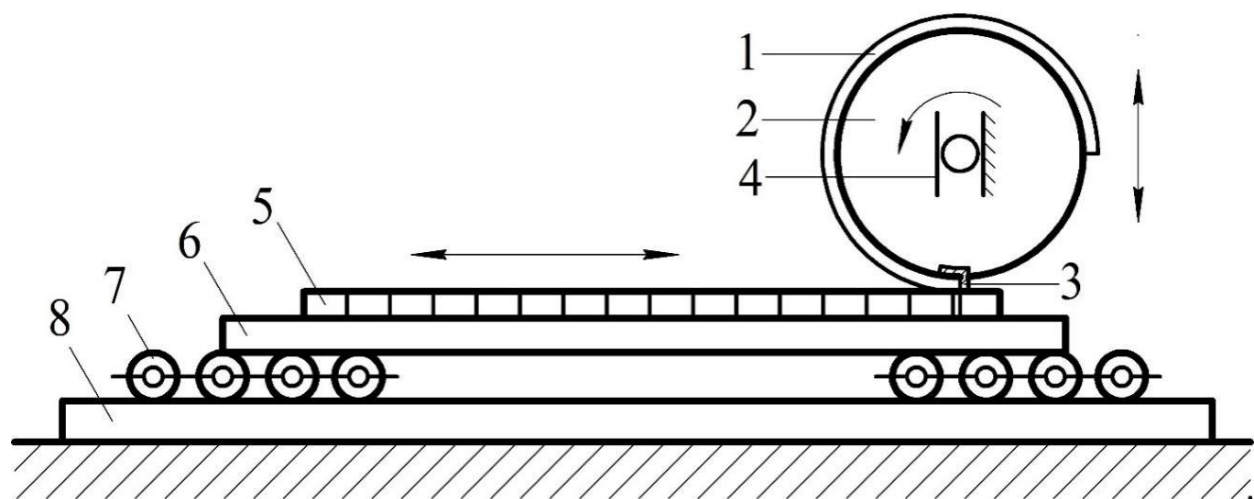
Графічна схема стоп-циліндрового висікального пресу 1 – заготовка палітурного матеріалу; 2 – металевий циліндр; 3 – затискачі; 4 – куліса; 5 – висікальна форма; 6 – талер; 7 – рольганг; 8 – нерухома станина
